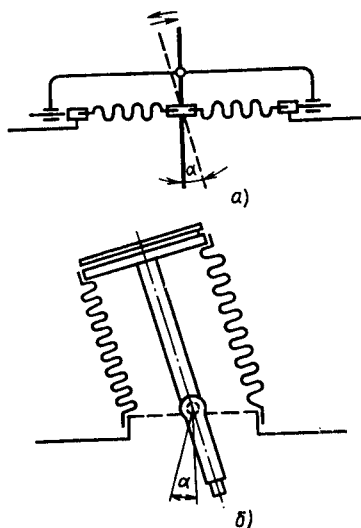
Схемы вводов качательного движения в вакуум:
